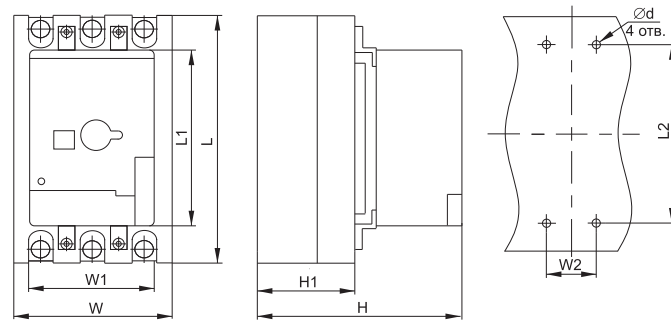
Габаритные размеры выключателей с установленным электроприводом / Figure 5 – Overall dimensions of circuit-breakers with electric drive installed
